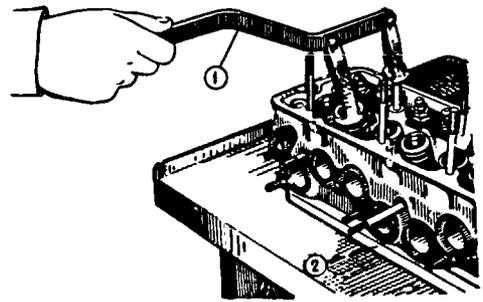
Снятие пружин клапанов: 1 - приспособление А.60311/Р; 2 - монтажная доска А.60335
